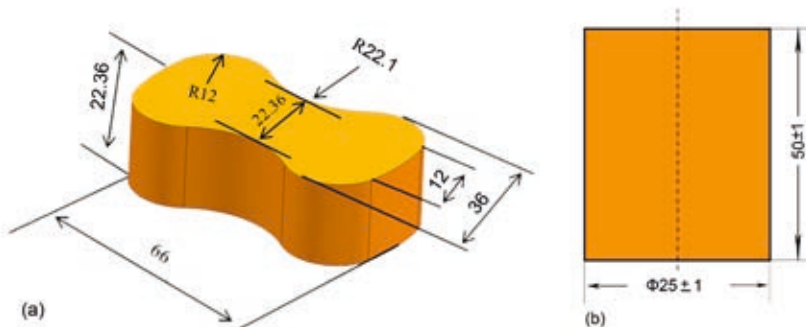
(a) Trækprøvens dimensioner (mm) og (b) trykprøvens dimensioner (mm)
